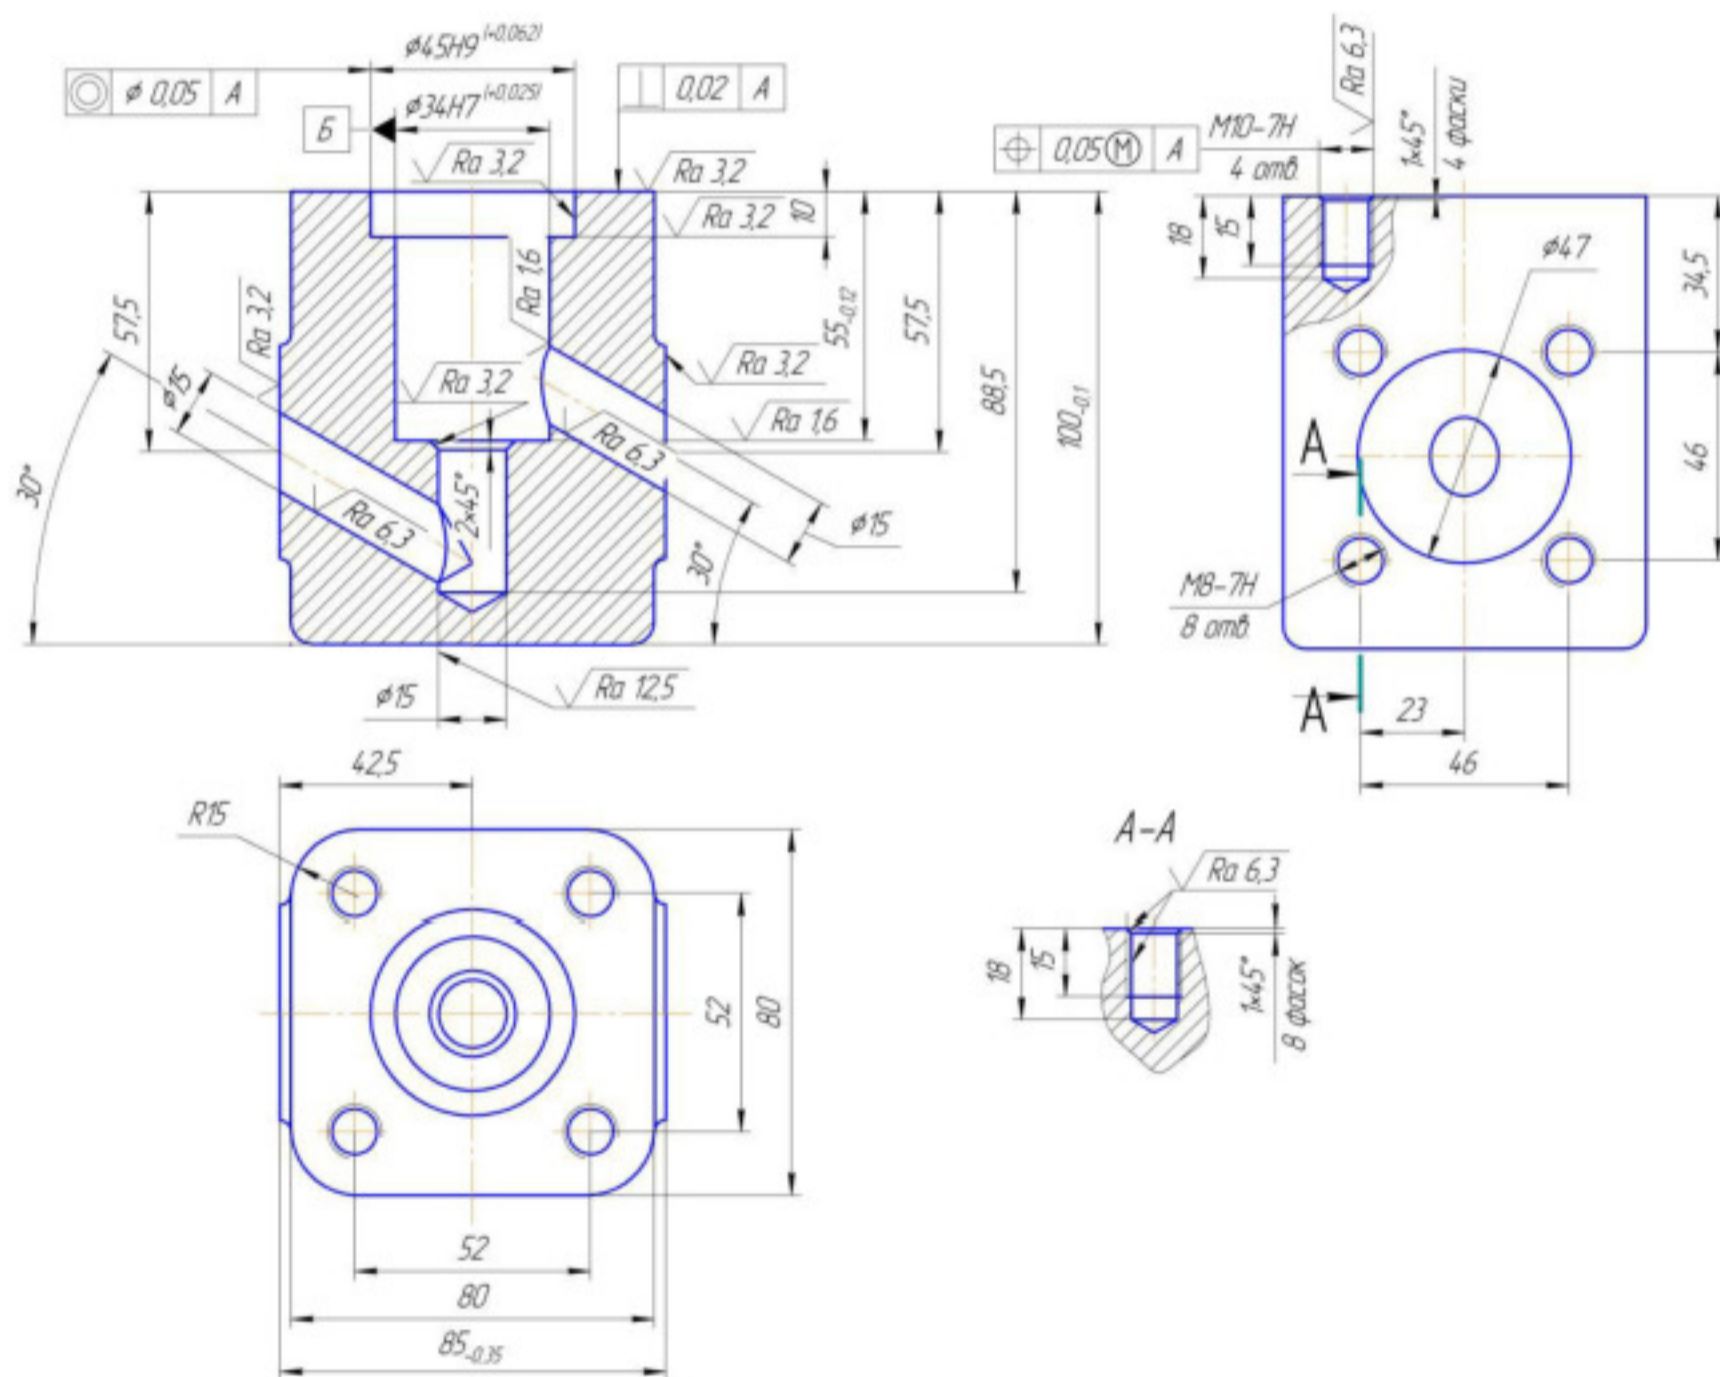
Деталь «Корпус ГР-004.55.001»
